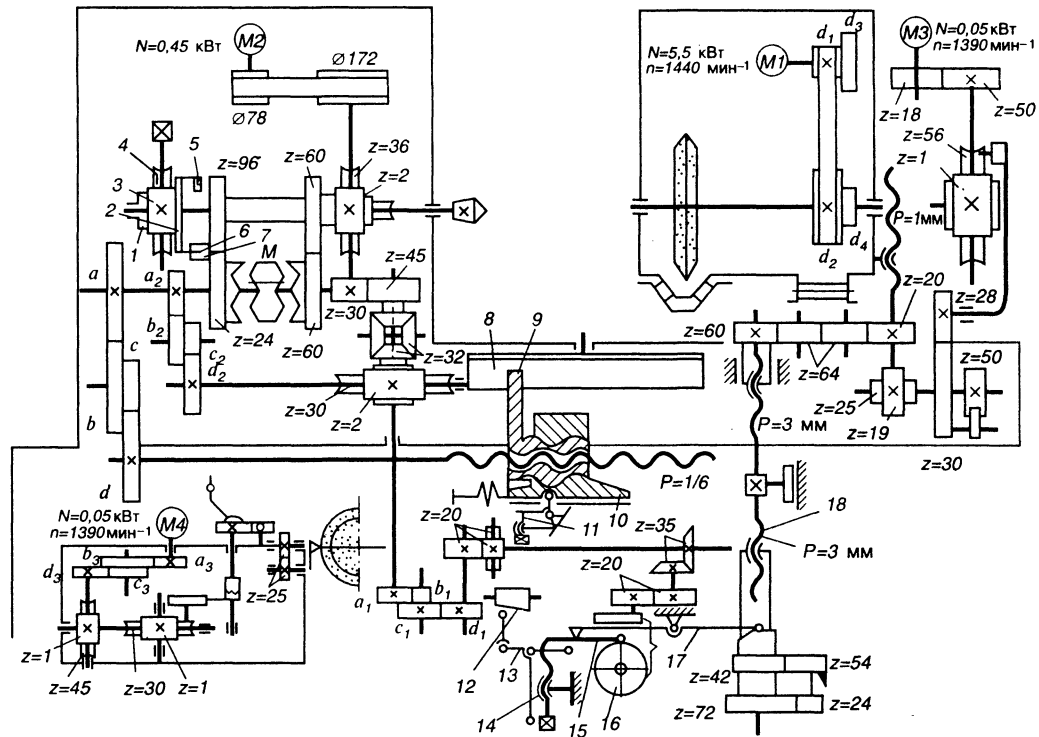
Кинематическая схема резьбошлифовального станка 5K822В
